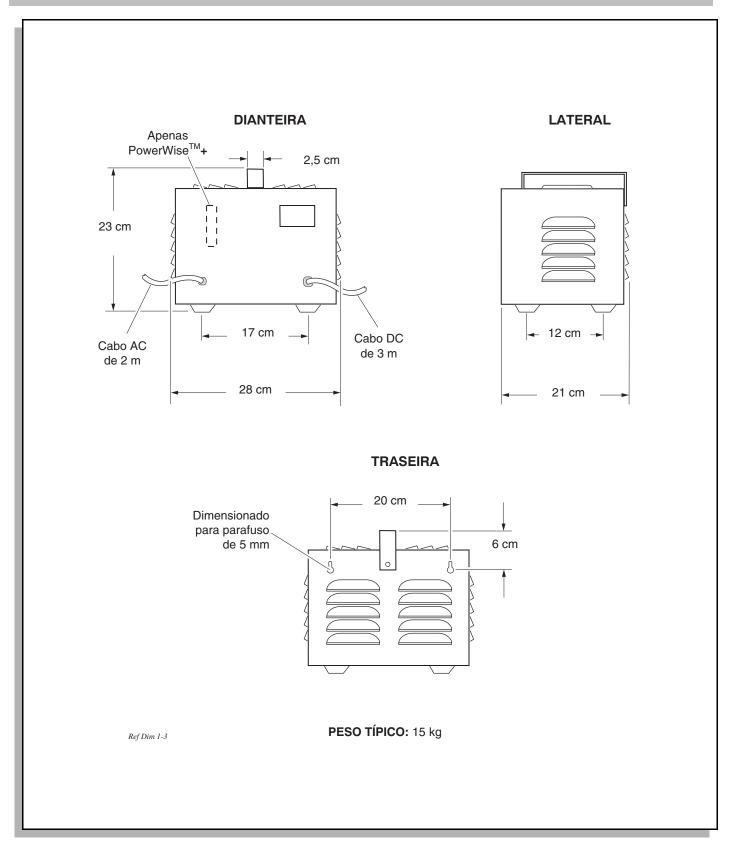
Dimensões do carregador portátil de bateria PowerWise™
